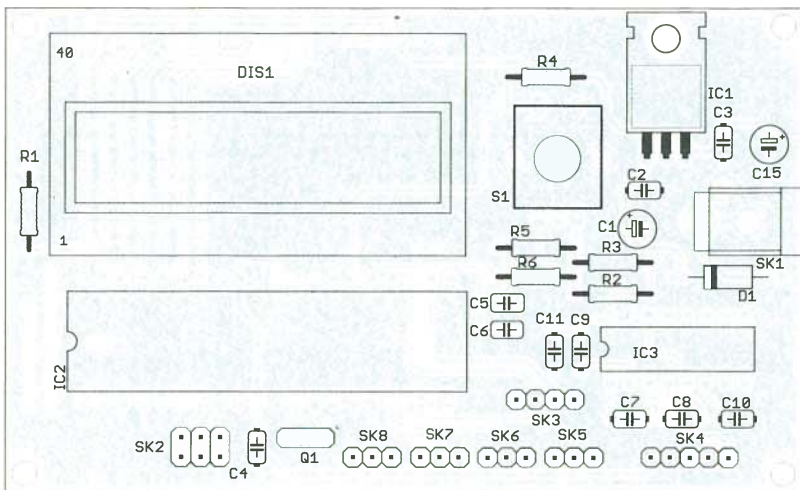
Bestückungsplan der beidseitig kaschiierten Controllerplatine; Abmessungen 105,7 mm x 64 mm, M 1:1
